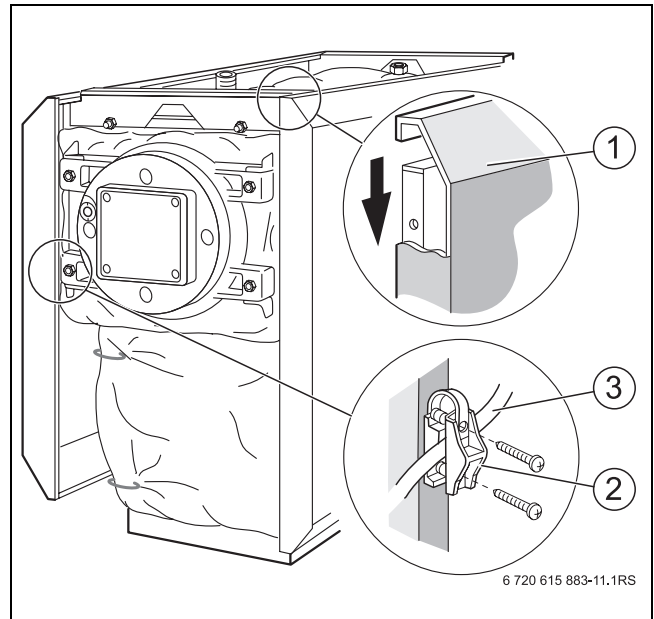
Установка боковых стенок и прокладка кабеля горелки
